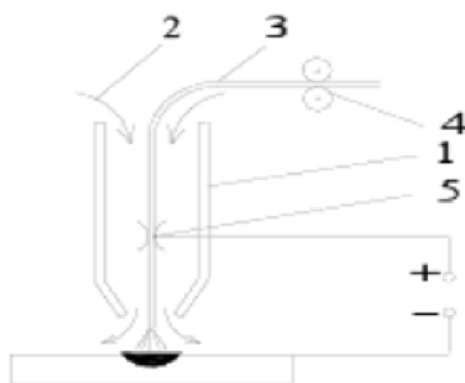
Схема процесса сварки в защитных газах плавящимся электродом
